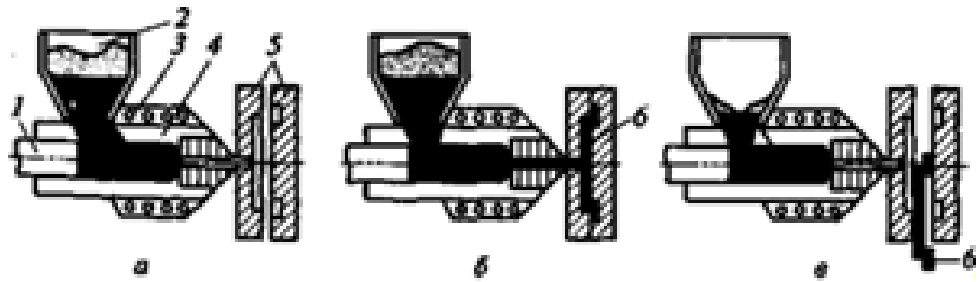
Схема роботи машини для лиття під тиском: плавлення сировинної маси; б - упорскування розплаву у форму; в - розмикання форми; 1 – поршень; 2 – завантажувальний бункер; 3 – нагрівачі; 4 – циліндр; 5 – роз'ємна форма; 6 - виріб
